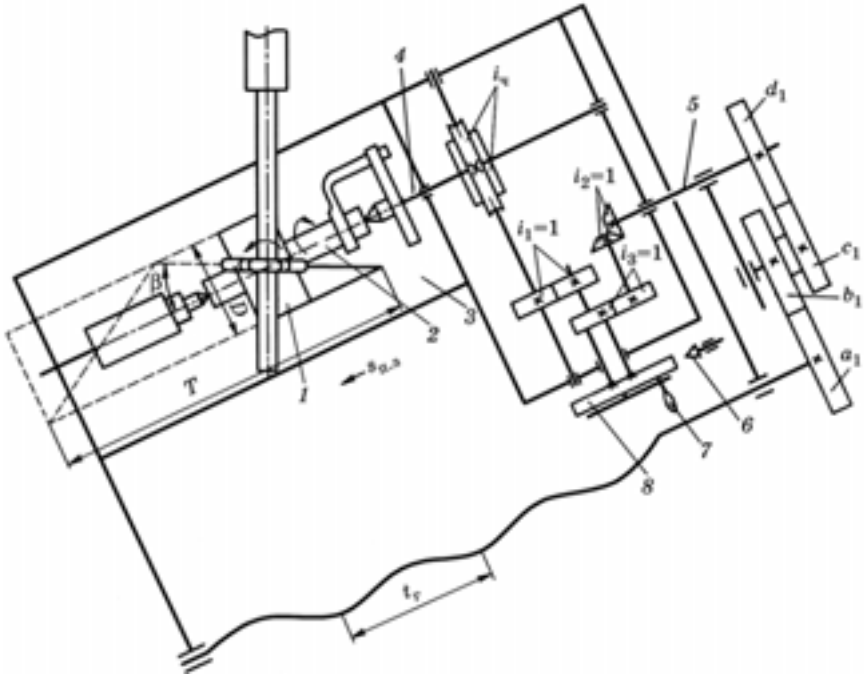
Схема налагодження універсально-фрезерного верстата і ділильної головки на фрезерування гвинтових канавок (косих зубів)
